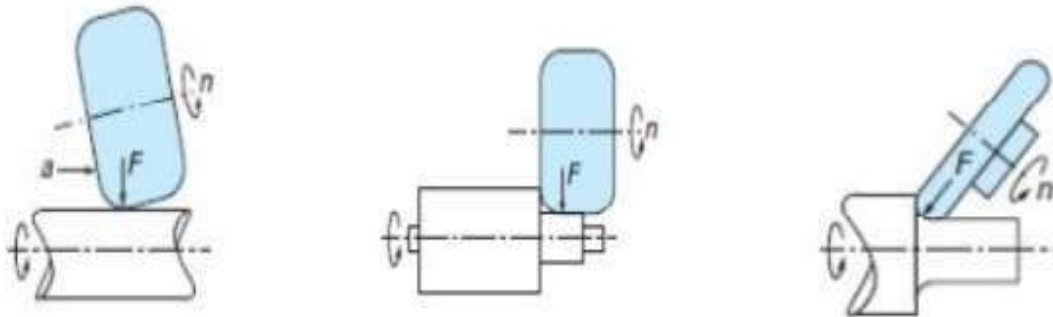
Outil du galetage commercialisé par la firme COGSDILL TOOL
